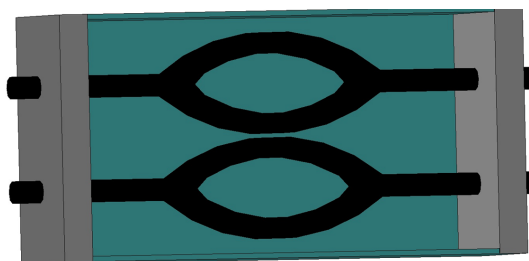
Схематичное изображение формы закладных элементов станины настольного станка для ультразвуковой сварки полимеров
